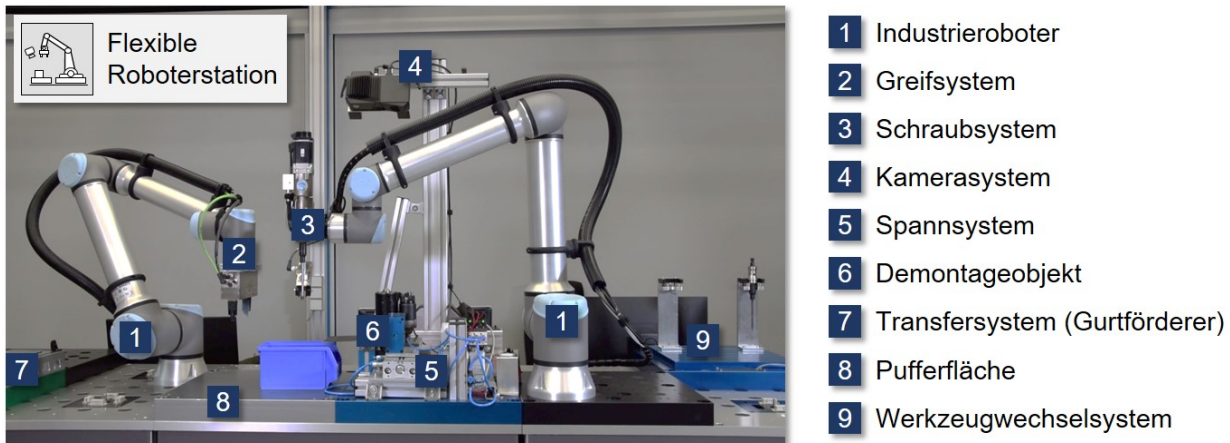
Prototyp einer flexiblen Roboterstation für die Demontage von Elektrokleinmotoren am Karlsruher Institut für Technologie
